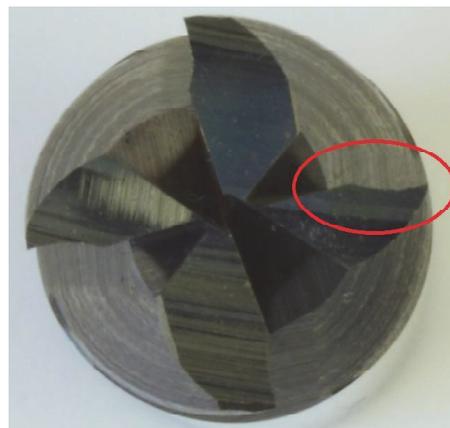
Зуб с наименьшей шириной задних поверхностей на цилиндре
